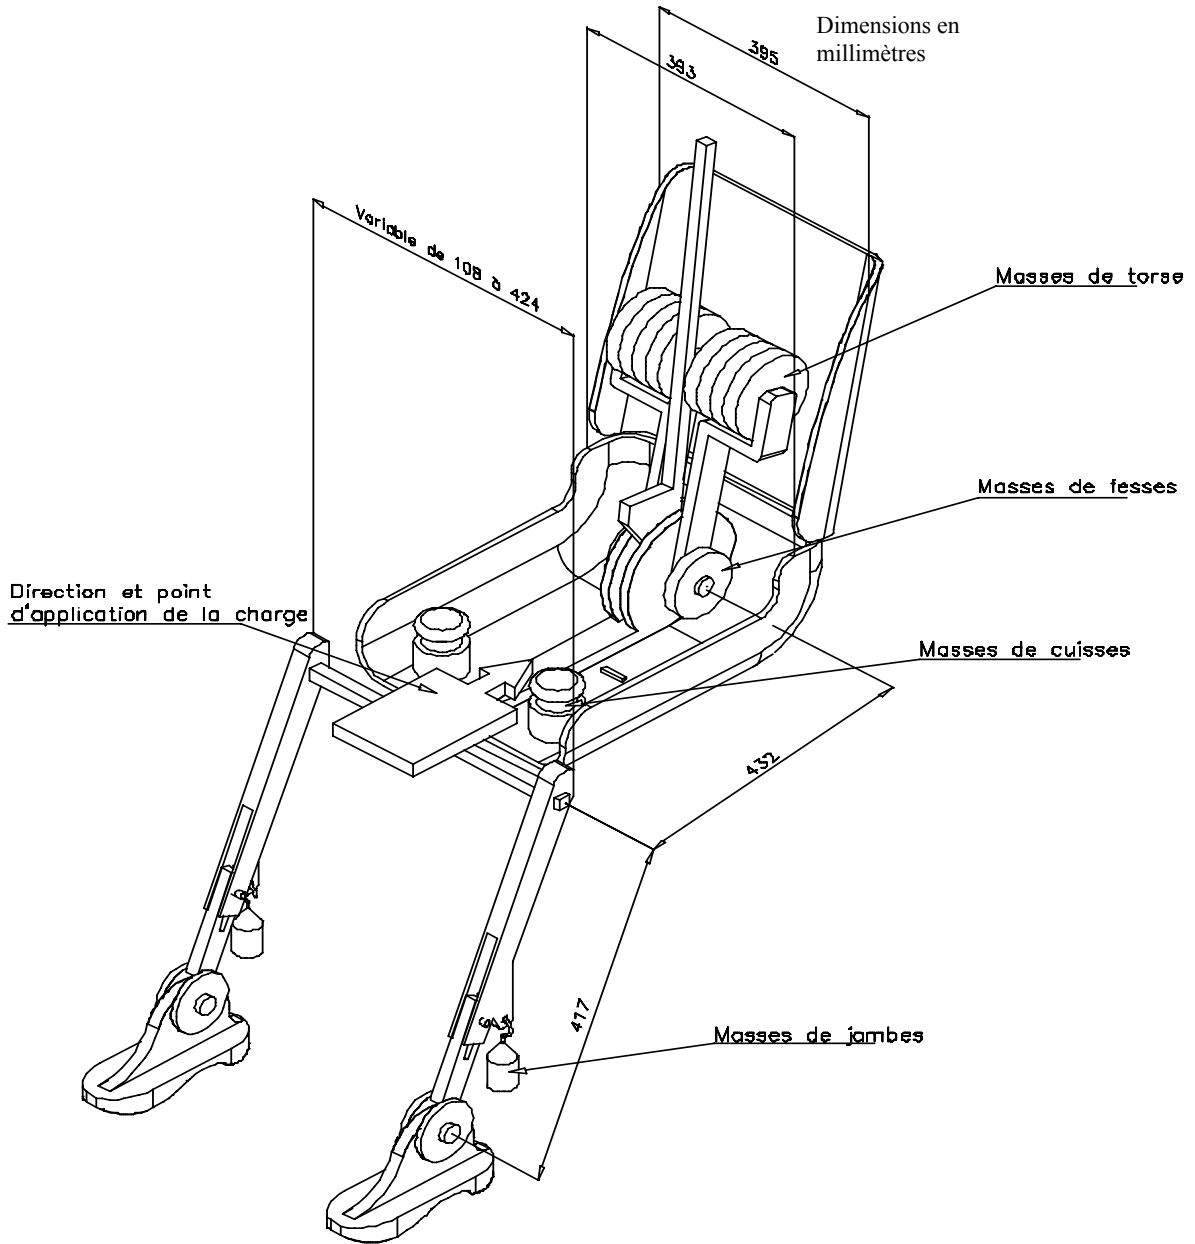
Dimensions des éléments de la machine 3-D H et emplacement des masses
